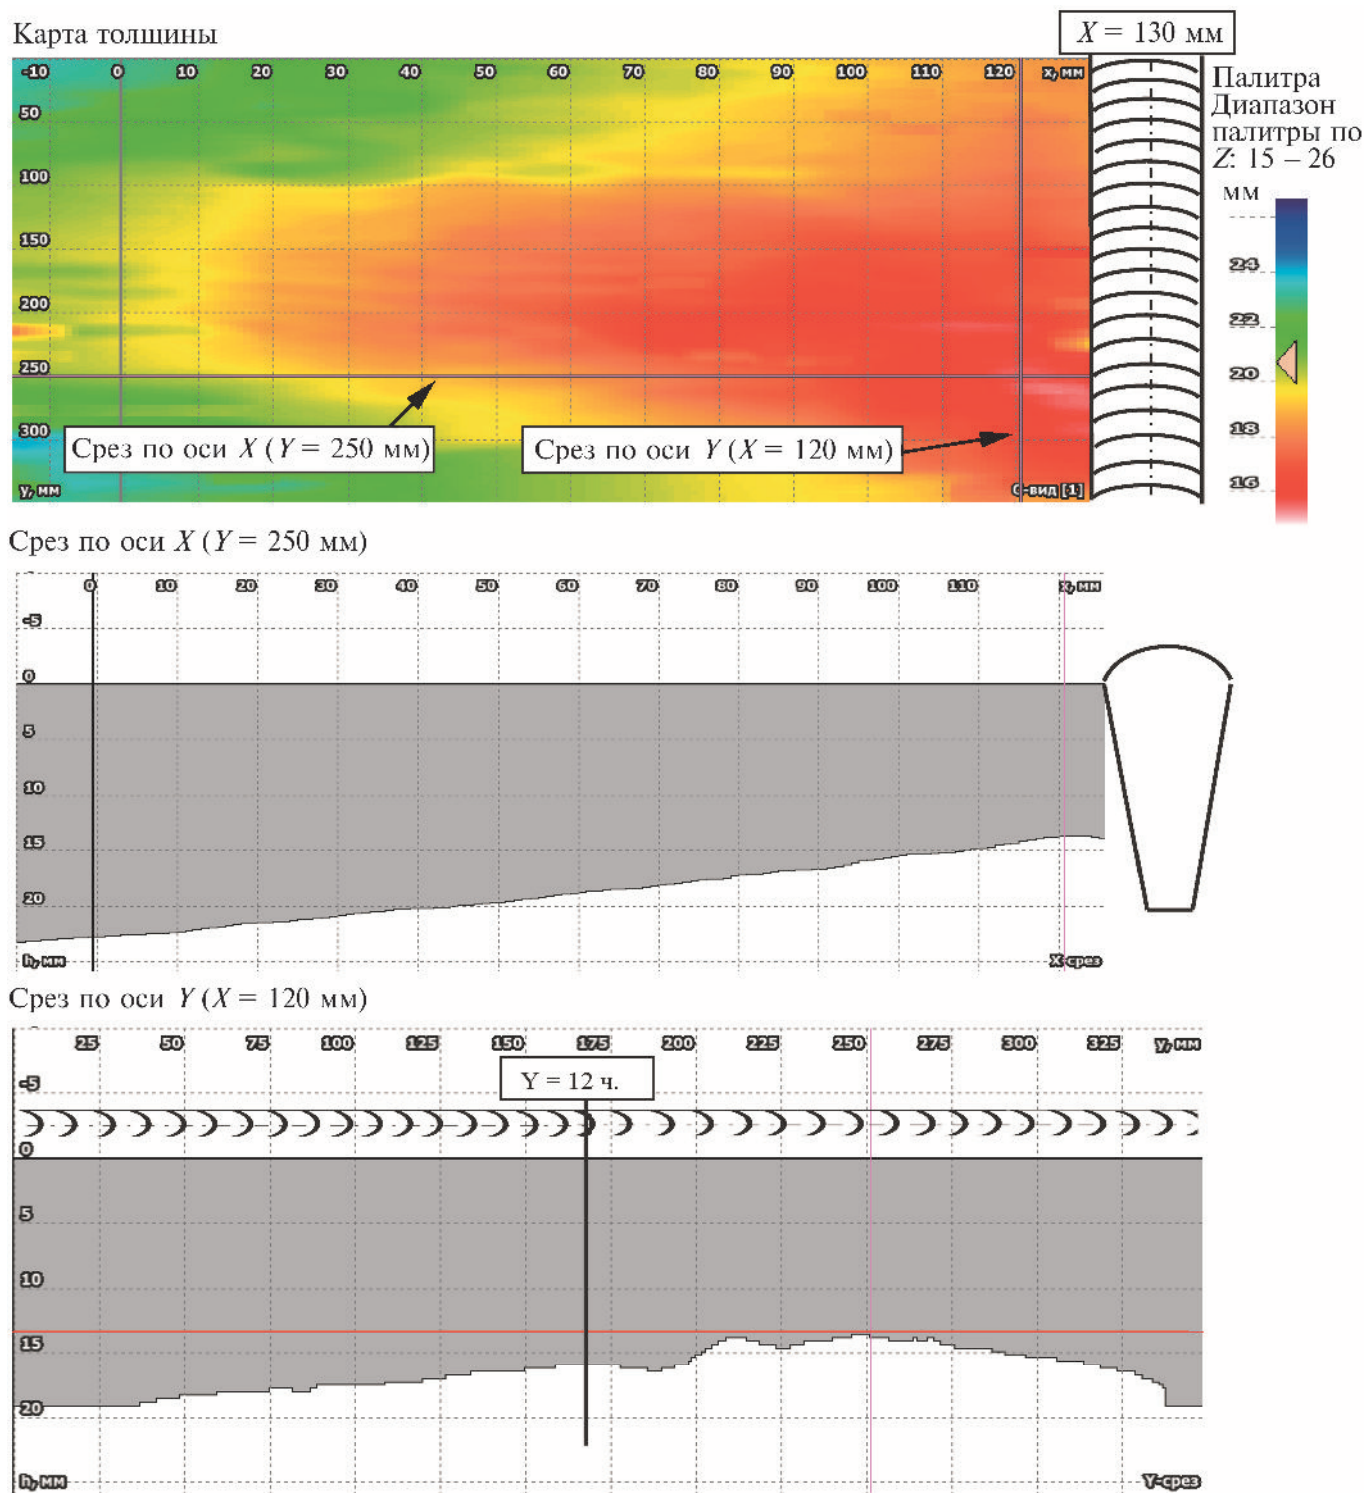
Карта толщины основного металла в околошовной зоне сварного соединения
